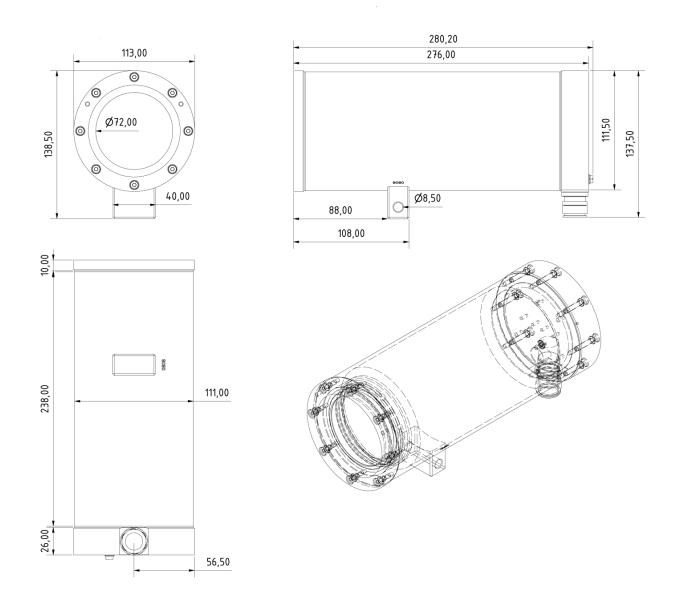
Abmessungen T08 ExCam IP135x mit K2 Flansch
